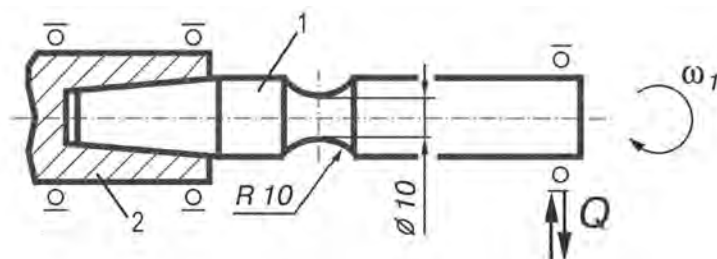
Общая схема испытаний на консольный изгиб с вращением
